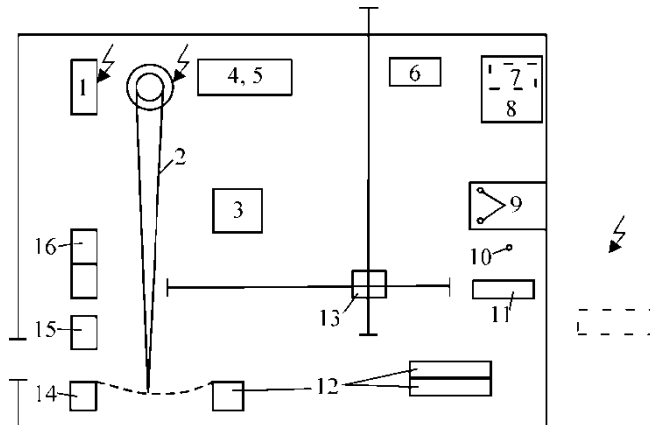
Робоче місце дефектувальника (площа 30 м²): 1 – верстат для прогонки різьби; 2 – кран консольний; 3 – контейнер для вилучених деталей; 4 – підставка під перевірочну плиту; 5 – плита перевірочна; 6 – шафа для матеріалів і вимірювального інструмента; 7 – дефектоскоп пересувний; 8 – стіл для дефектації деталей; 9 – рольганг (загальний для робочих місць); 10 – стілець підйомно-поворотний; 11 – стіл конторський; 12 – стелаж для складальних одиниць; 13 – кран-балка електрифікована підвісна; 14 – стелаж для деталей; 15 – ящик для піску; 16 – ящик для обтирального матеріалу.
